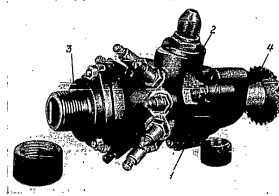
Распределитель сжатого воздуха с приводом счетчика оборотов.
